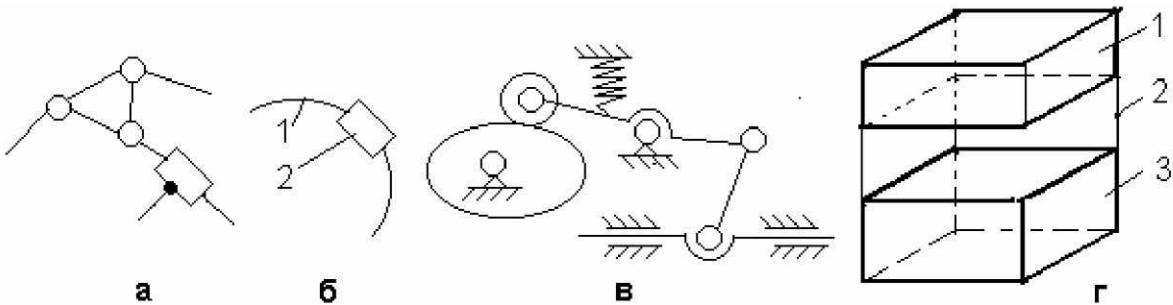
Схемы: а – кинематической цепи; б – кинематической пары; в – механизма; г – подвижного соединения
